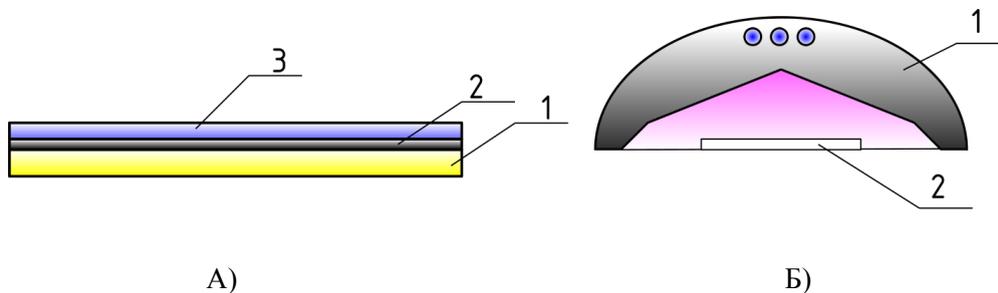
А) заготовка: 1 – диэлектрическое гибкое основание, 2 – слой алюминия, 3 – плёнка фоторезиста; Б) УФ-лампа с заготовкой, 1 – УФ-лампа, 2 – заготовка
